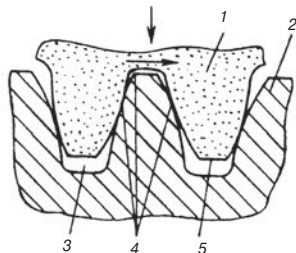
Беззазорное двухпрофильное зацепление зубьев хона и заготовки.
